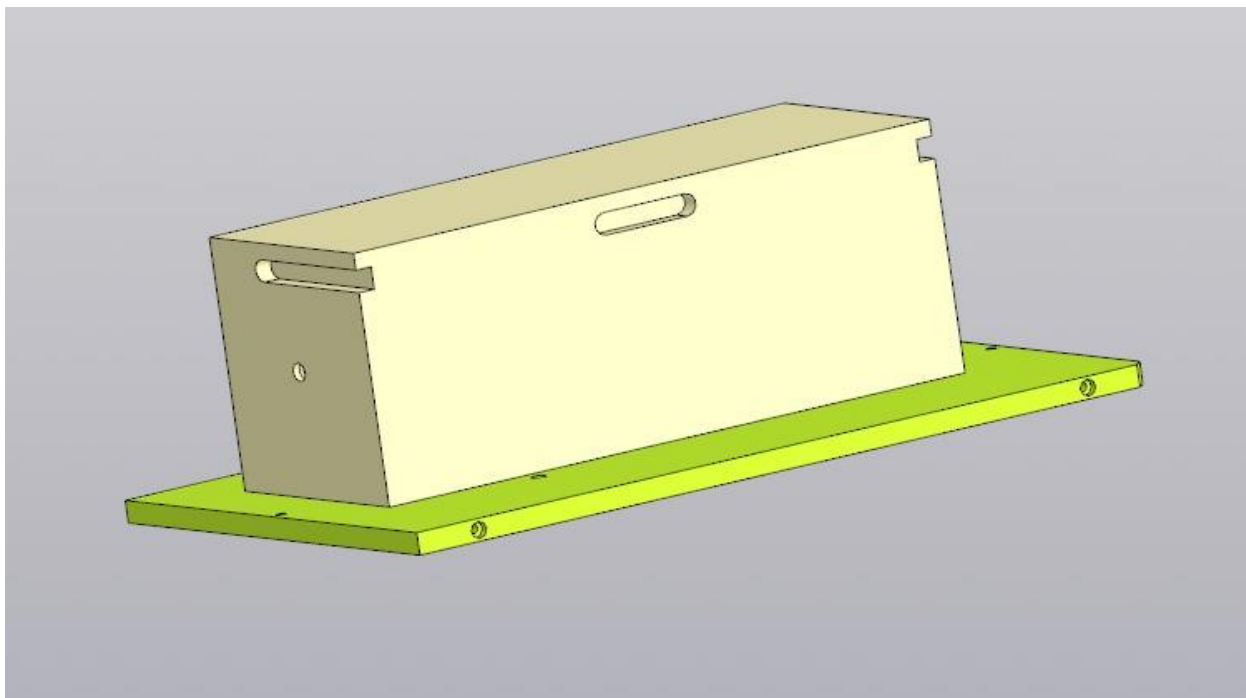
3D-модель заготовки калибра после фрезерной обработки
